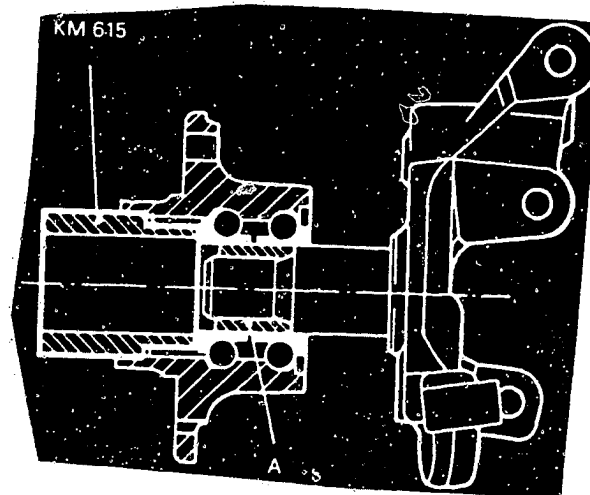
Montage einer neuen Naben-Lager-Einheit mit Spezialwerkzeug. Die Hülse A darf vor der Montage nicht entfernt werden.
